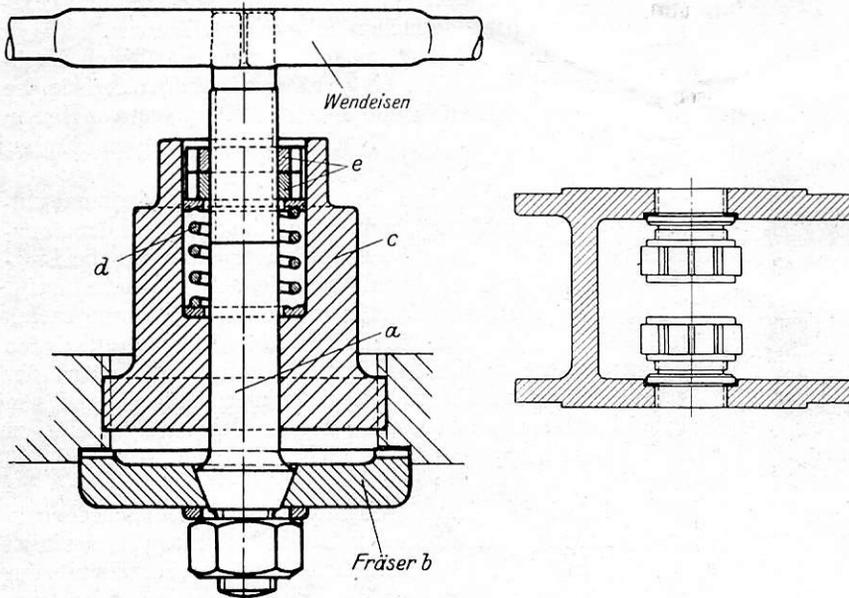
Fräser für Luftpumpen-Instandsetzung.
